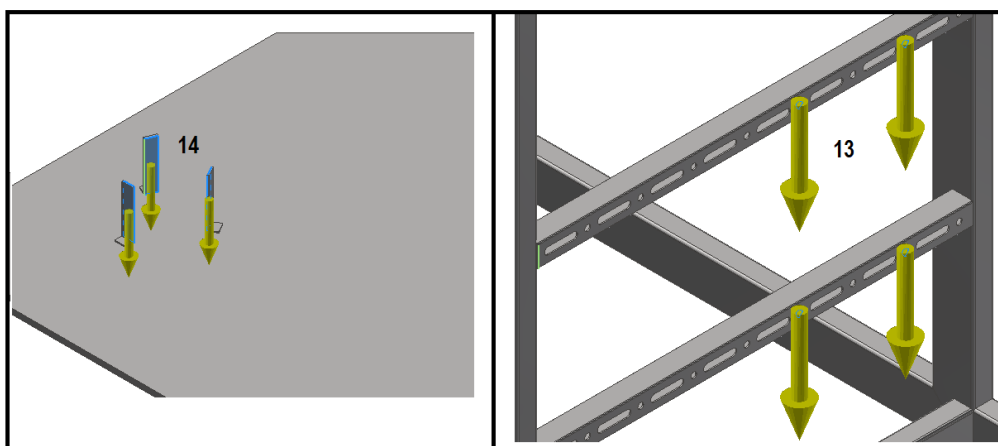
Pormenor das cargas aplicadas na estrutura (b)
